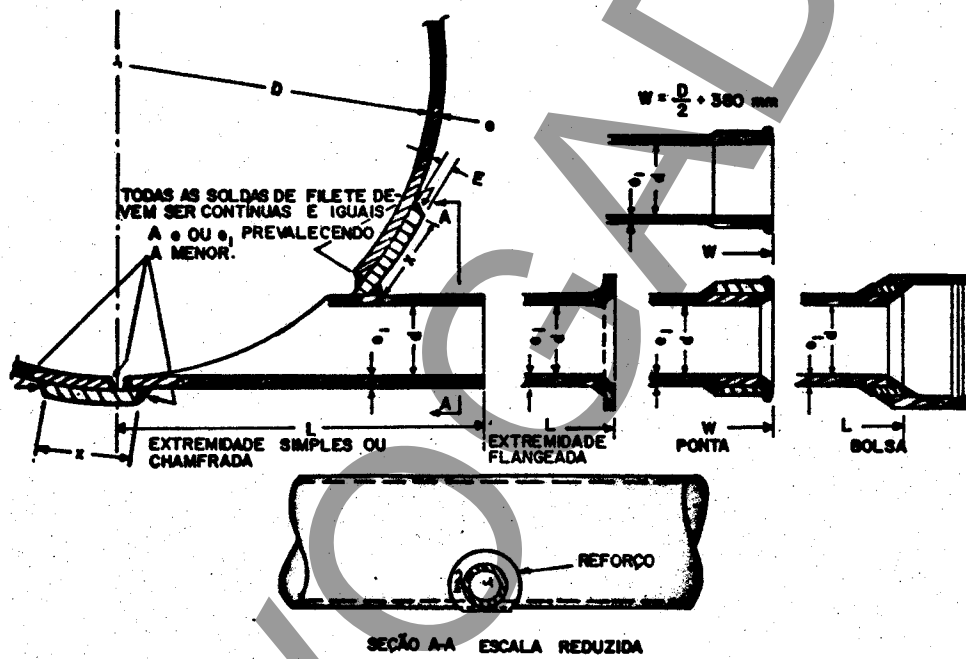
DERIVANTES TANGENCIAIS DE AÇO SOLDADO
